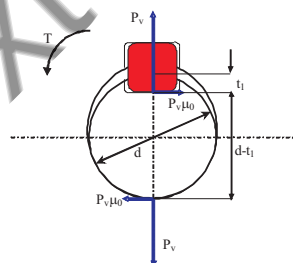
Dimensões referentes a chaveta em um eixo.
